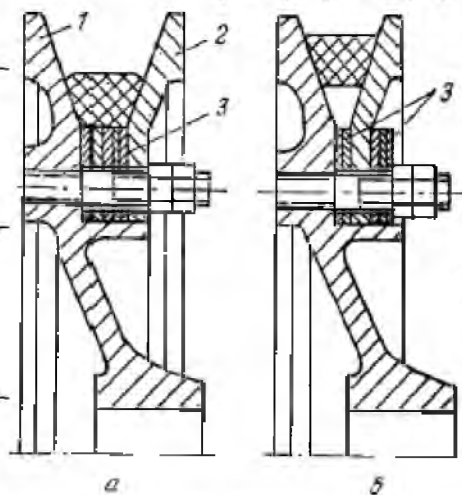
Регулювання натягу приводного ременя компресора: а — зменшення натягу; б — збільшення натягу; 1 — шків; 2 — шпека; 3 — регулювальні прокладки.
